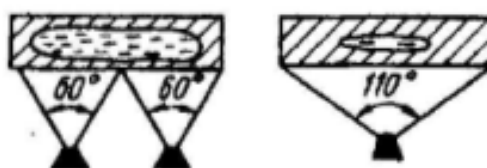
Схема расположения форсунок по ширине заготовки с разными углами раскрытия
